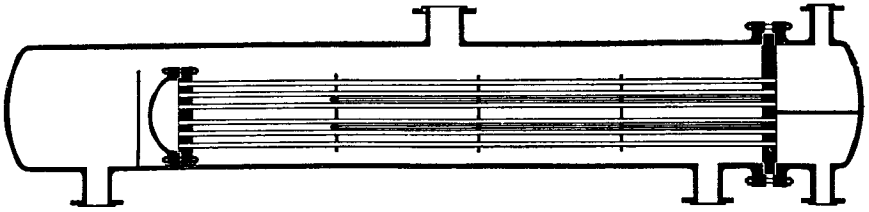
Caldereta tipo marmita *con espejo integral.* (*Patterson Foundry and Machine Co.*)
